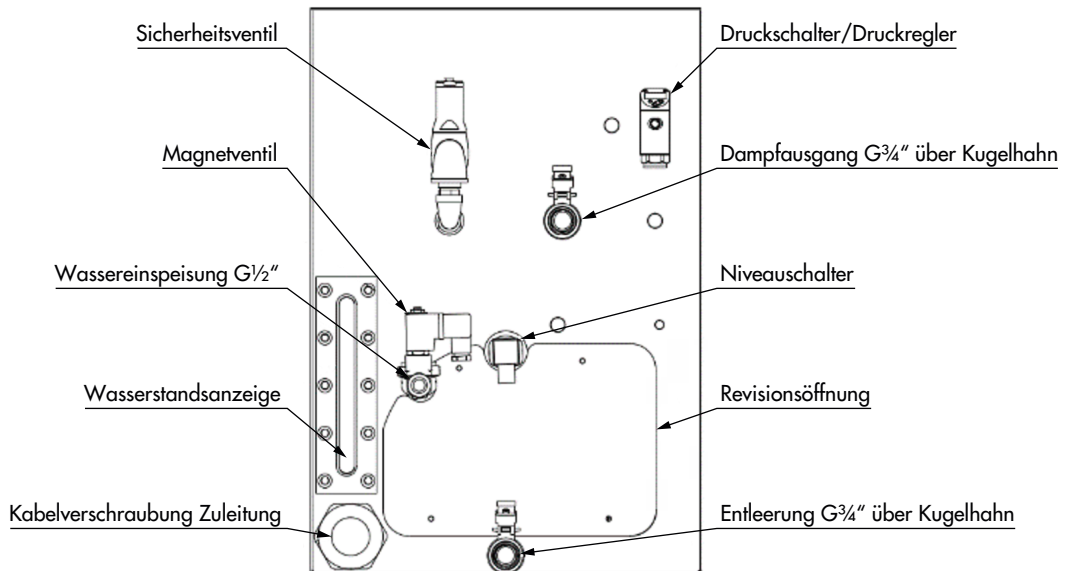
Elektrischer Dampferzeuger Typ 7121 · Anschlüsse
